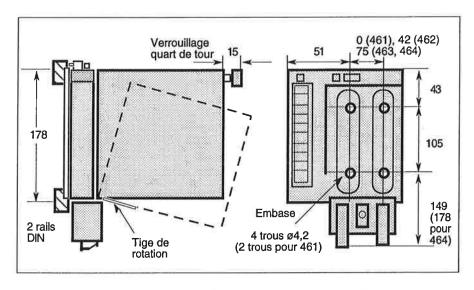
Cotes de fixation sur une paroi verticale (mm)
